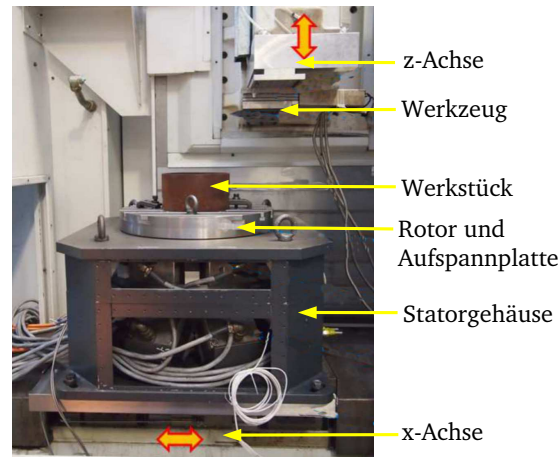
Funktionsbaugruppen einer Werkzeugmaschine [14]
